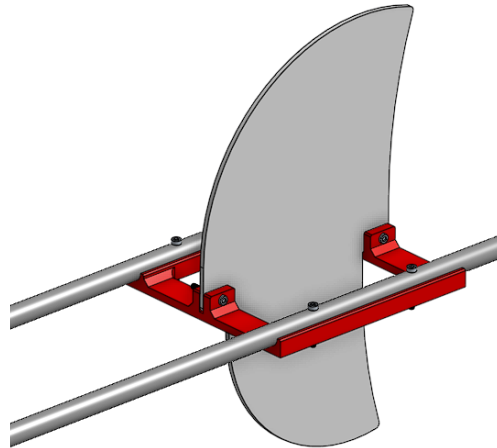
Vista isométrica 2 del ensamblaje de la estructura de la cola en Onshape [fuente: elaboración propia]
